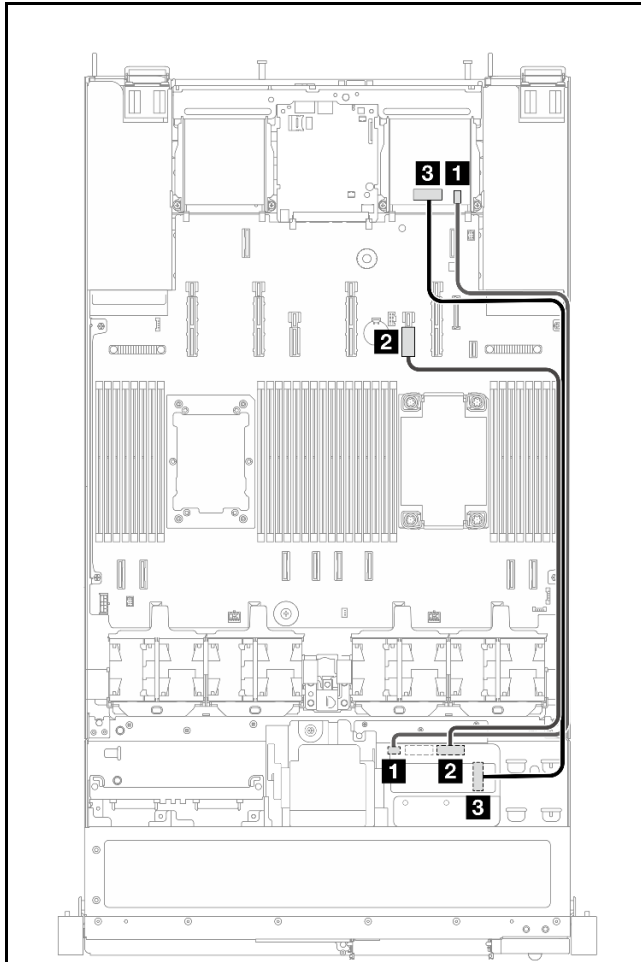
Kabelführung für x8 OCP-Interposerkarten
